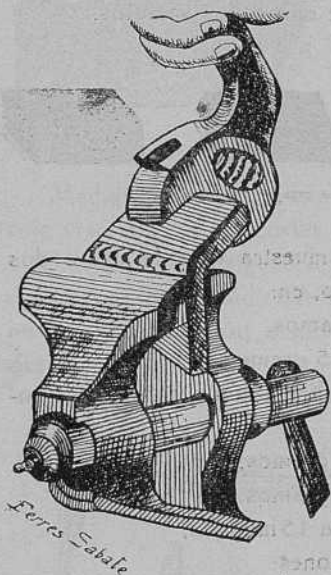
Ensayo de una soldadura doblándola por la línea soldada,
